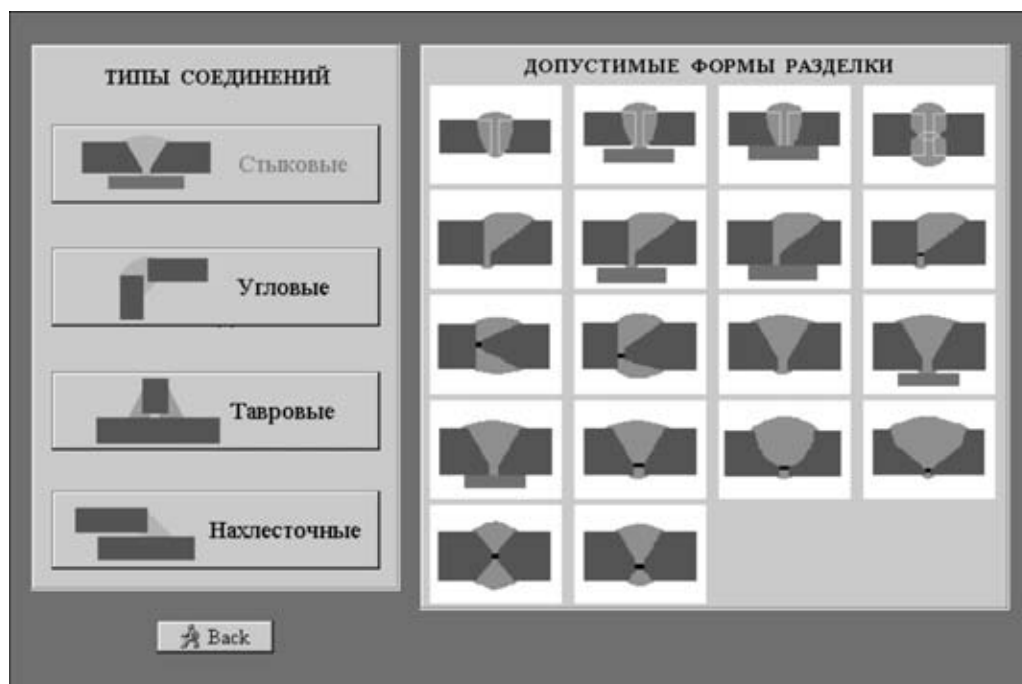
Выбор типа сварного соединения и формы разделки кромок при сварке легких сплавов
